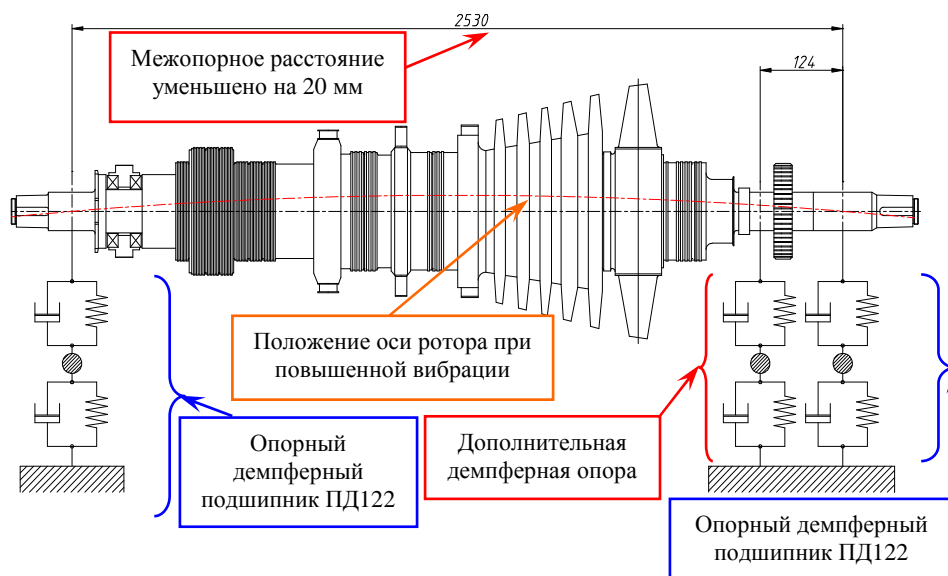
Схема ротора со смещенными демпферными подшипниками и дополнительной демпферной опорой ТРИЗ®
